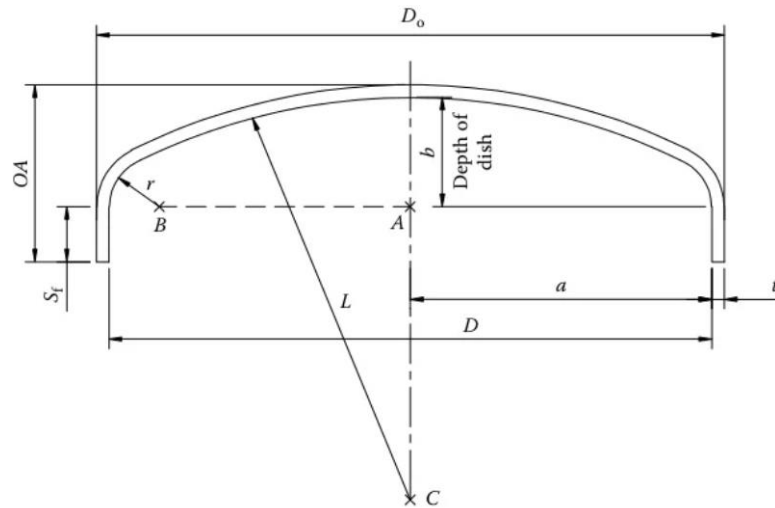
Detalles dimensionales de la cabeza toriesférica [22]
